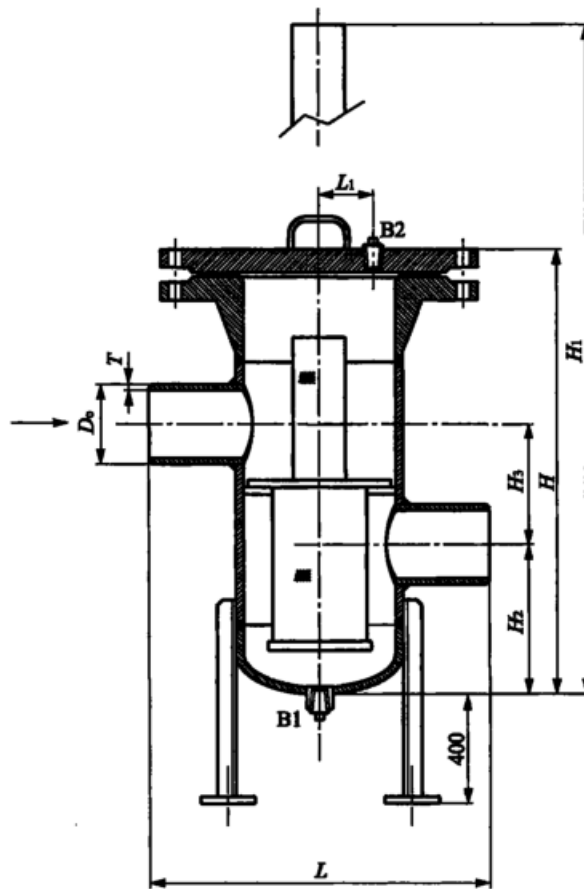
焊接连接多滤筒式篮式过滤器结构
